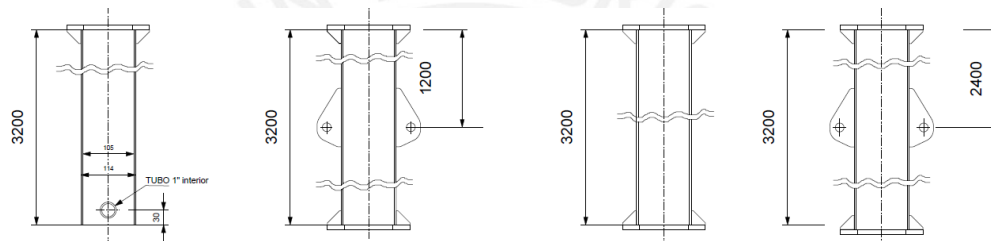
Modelo geométrico de la torre, por partes y ensamblada.
